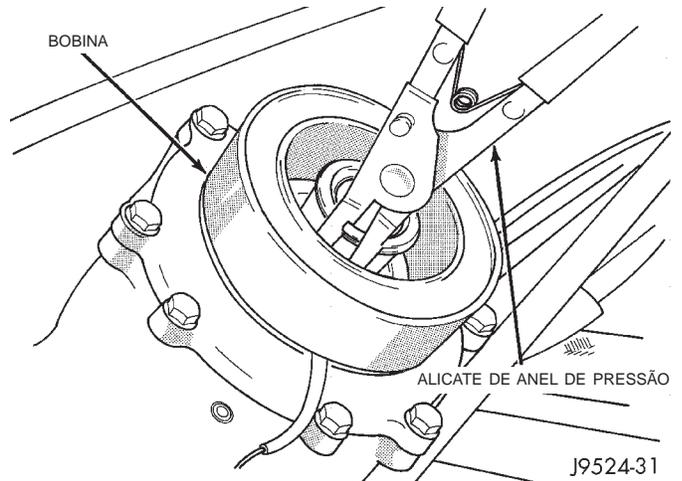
Remoção do Anel de Pressão da Bobina de Campo do Acoplador
